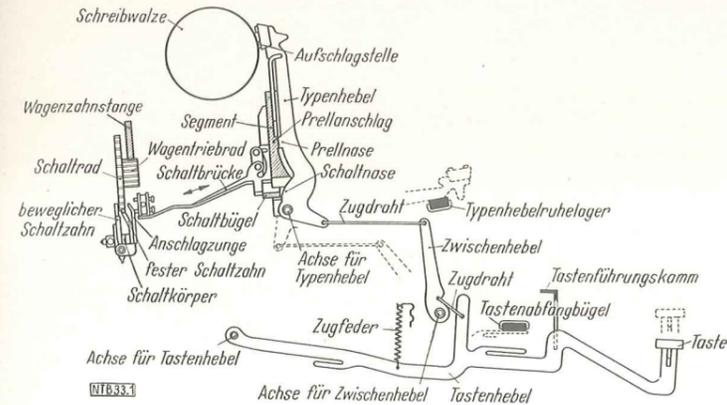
Zusammenwirken von Typenhebelgetriebe und Schrittschaltwerk bei der Optima-Schreibmaschine. Schaltung durch den Typenhebel [1]
